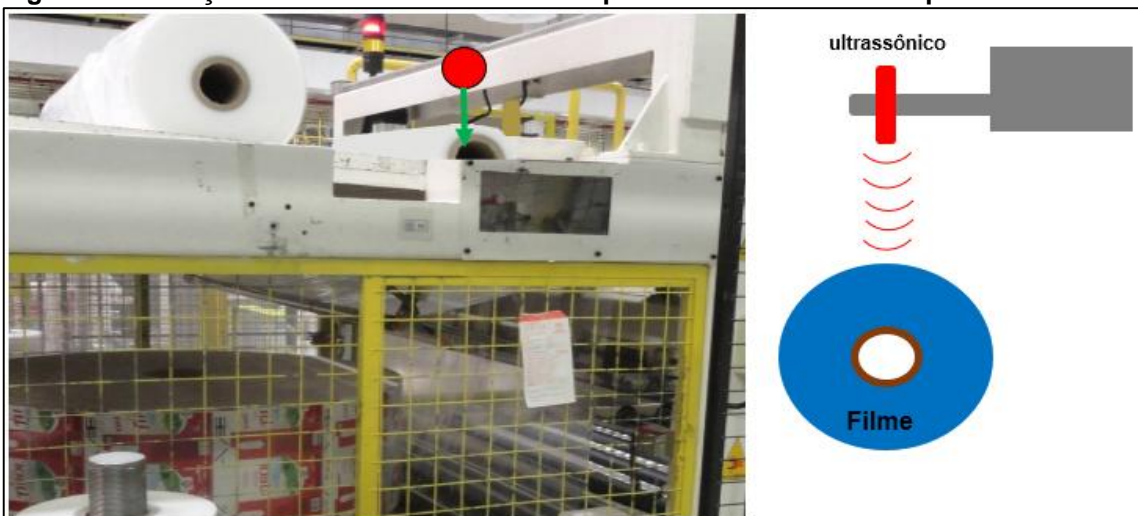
Posição definida do sensor US1300 para o filme horizontal inferior
